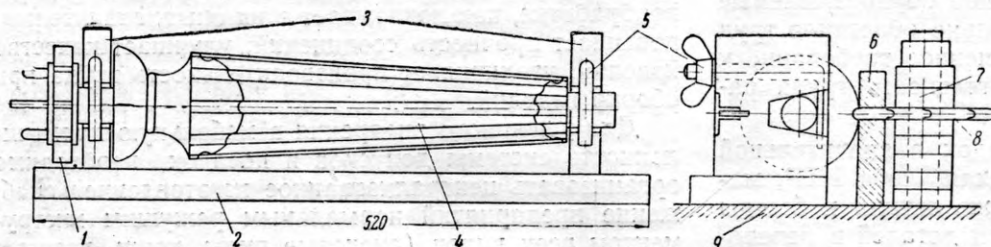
Схема приспособления для фрезерования канавок на колонках:
